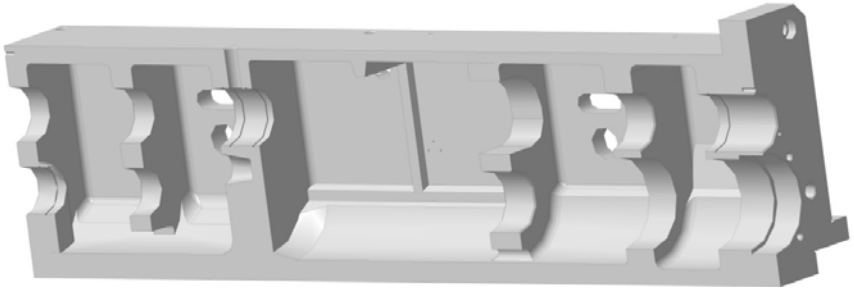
3D-модель корпусу горизонтальної шпindelьної бабки.
